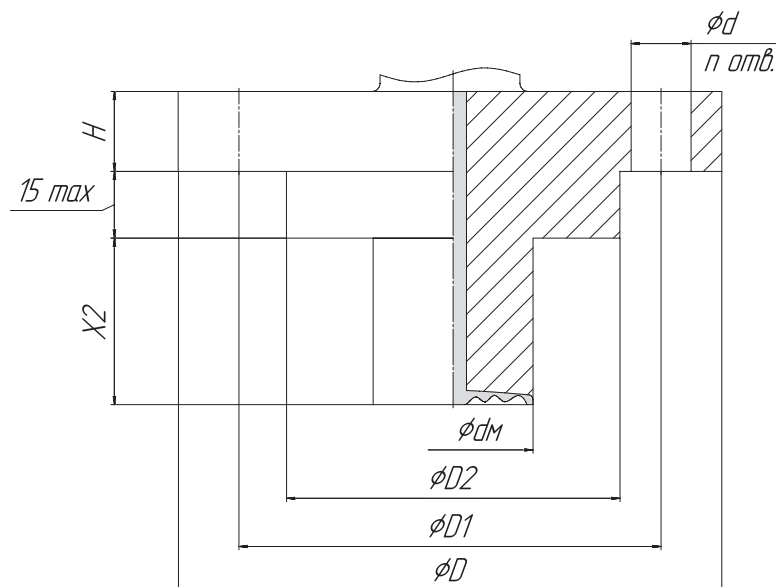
Габаритные и присоединительные размеры фланцев с плоской мембраной по DIN EN 1092-1
